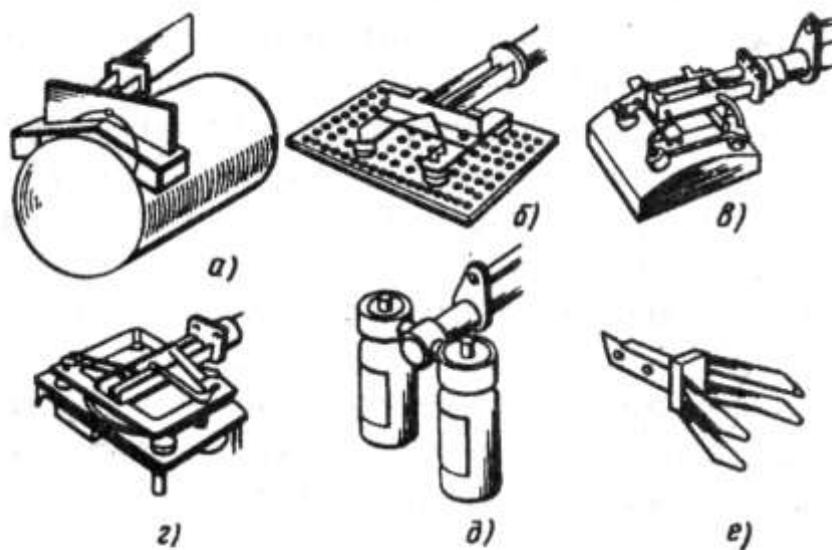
Захватные устройства: а и б — электромагнитные; в и г — вакуумные; д и е — с эластичными камерами
